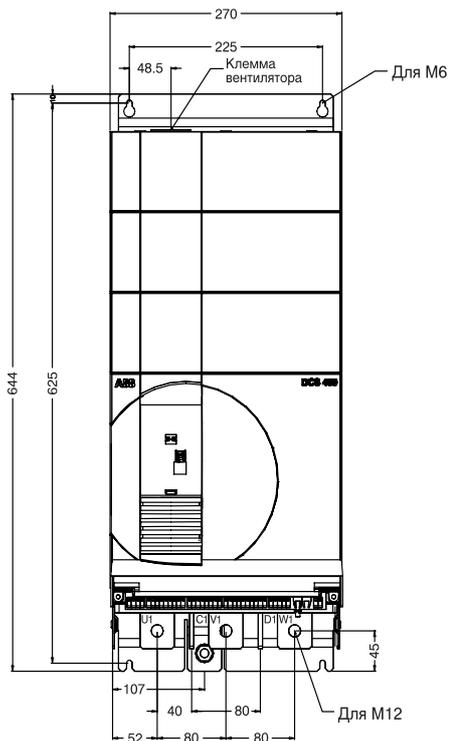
/1: Габаритный чертеж модуля А1, А2, А3
